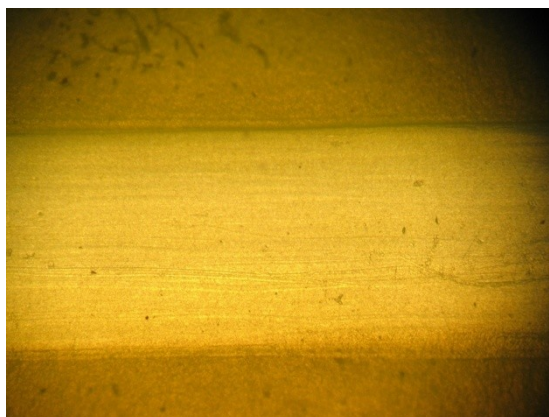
Внешний вид сварного шва листового полиэтилена выполненного УЗ сварочным аппаратом с чопперным регулятором
